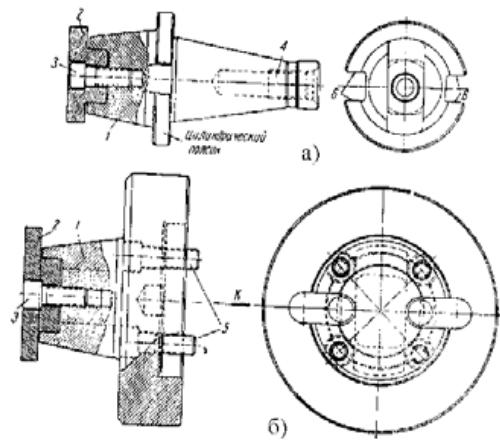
Оправки для закріплення торцевих фрез до шпинделя фрезерного верстата (а – кріпиться в конічному отворі шпинделя фрезерного верстата; б – кріпиться до торця шпинделя фрезерного верстата)
